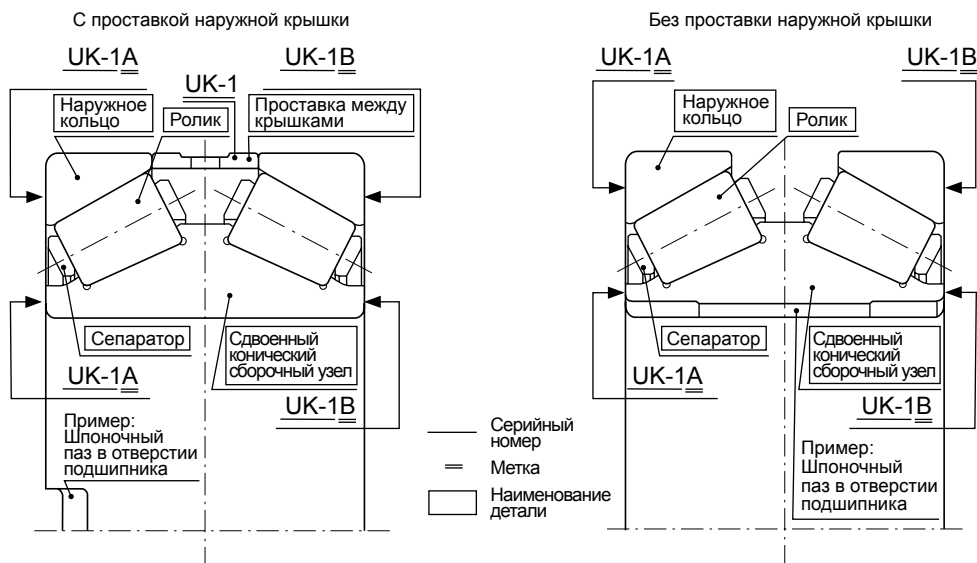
Наименование деталей и примеры маркировки (двухрядный конический роликоподшипник с максимальновозможным углом контакта)
